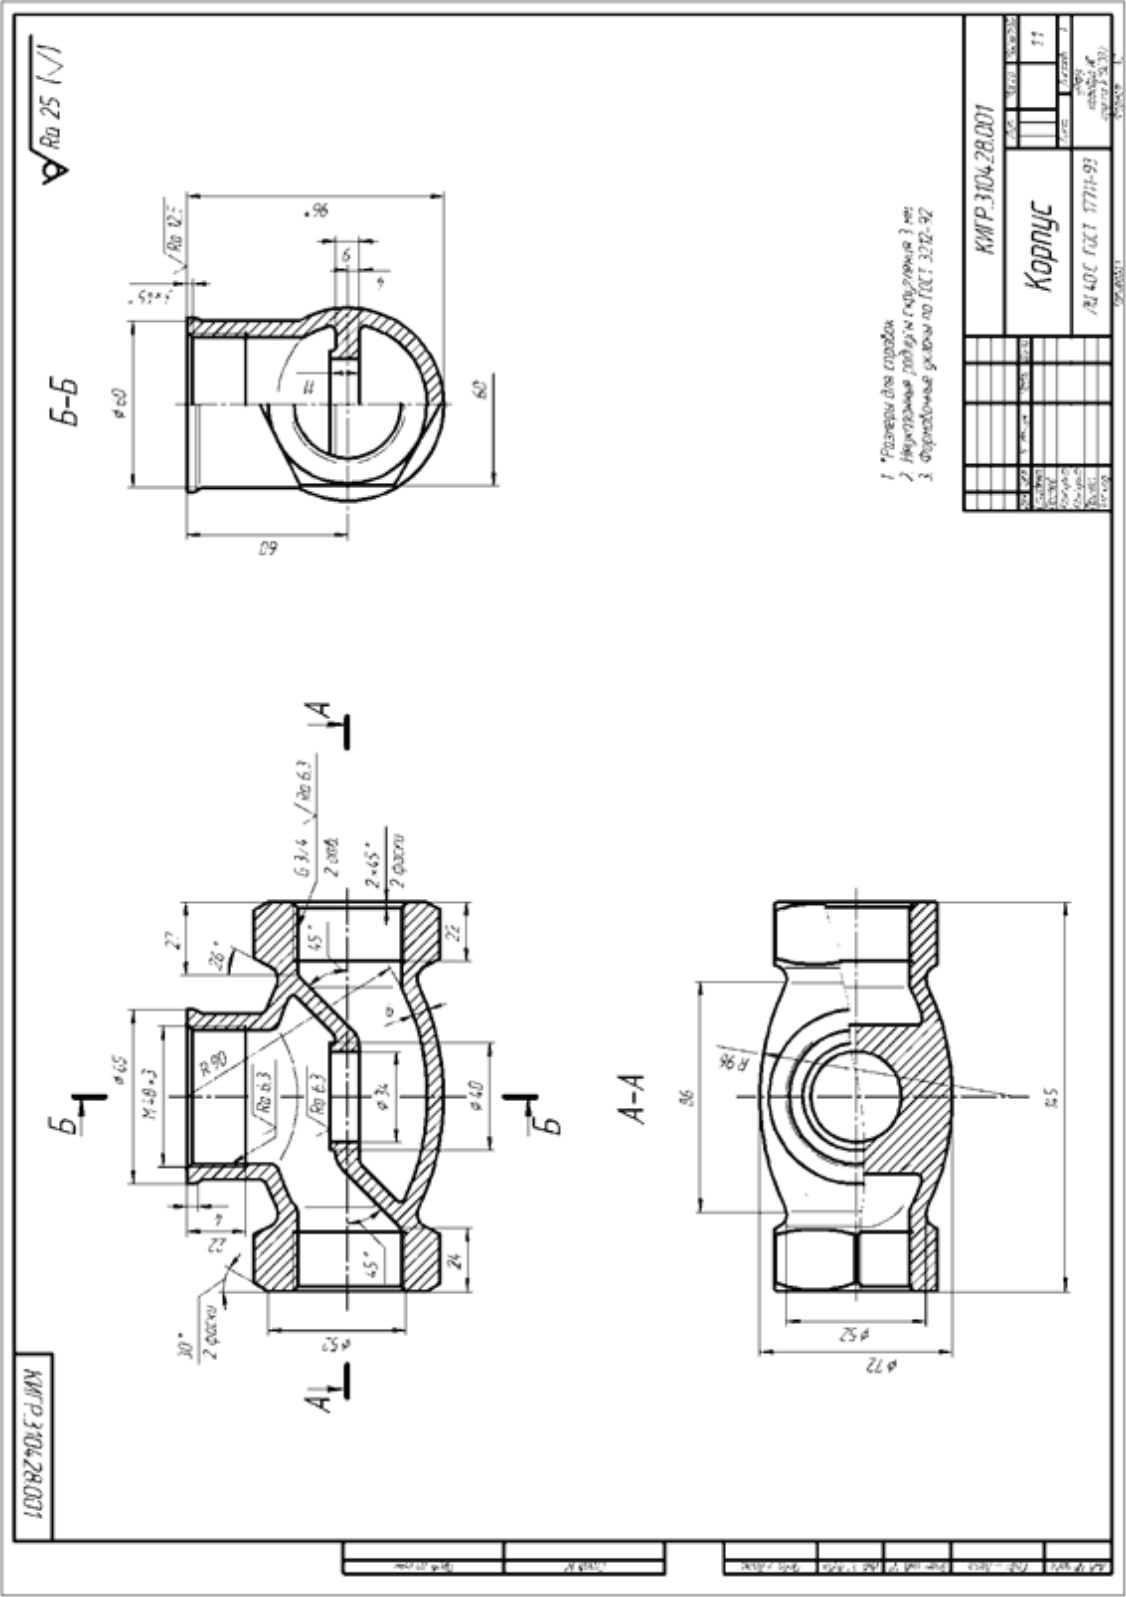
Пример учебного чертежа корпуса литой детали «Корпус»
